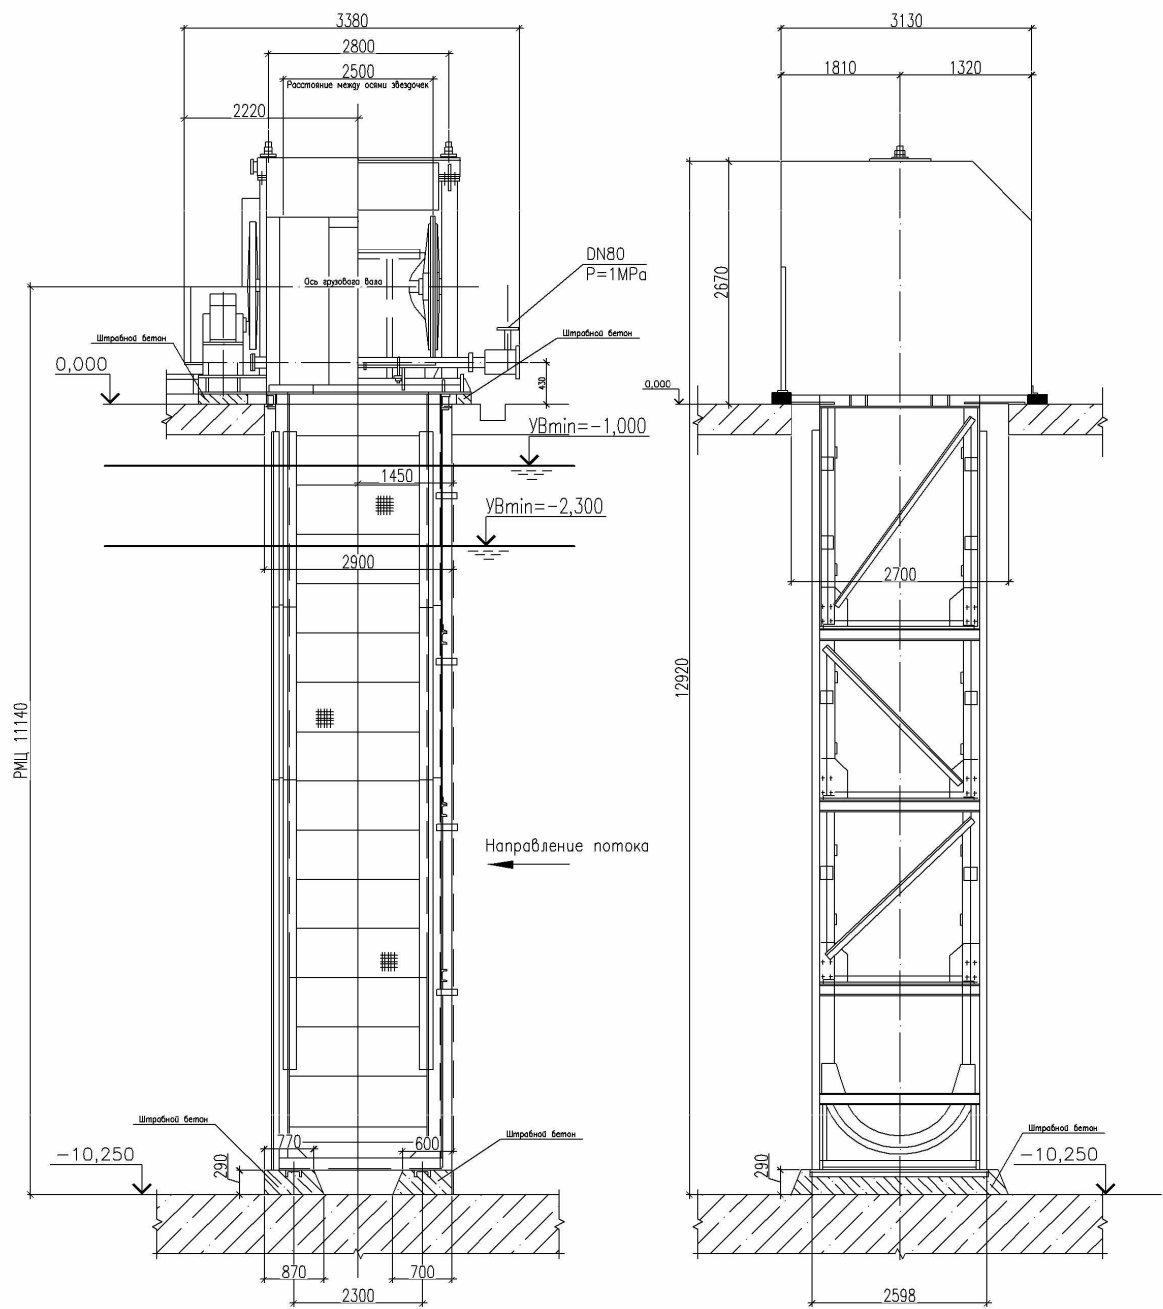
Габаритный чертеж машины водоочистой
